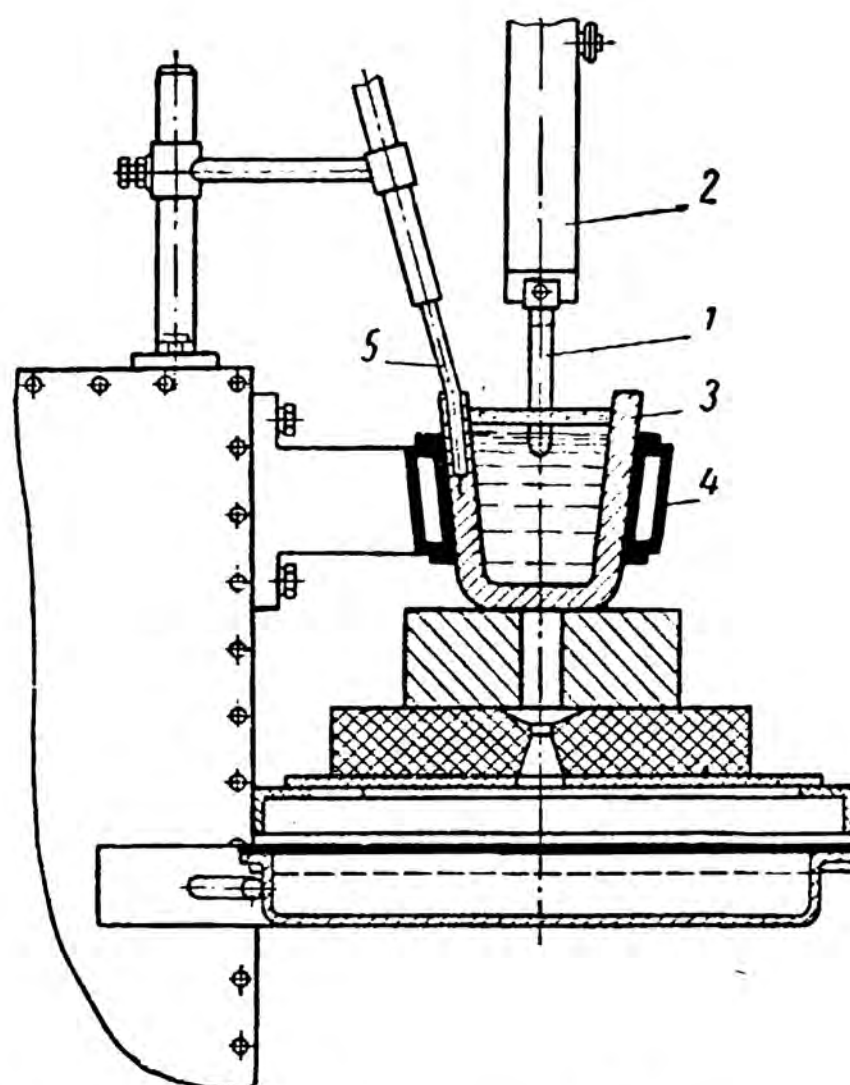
Схема процесса пайки и конструкция тигля роторного полуавтомата
